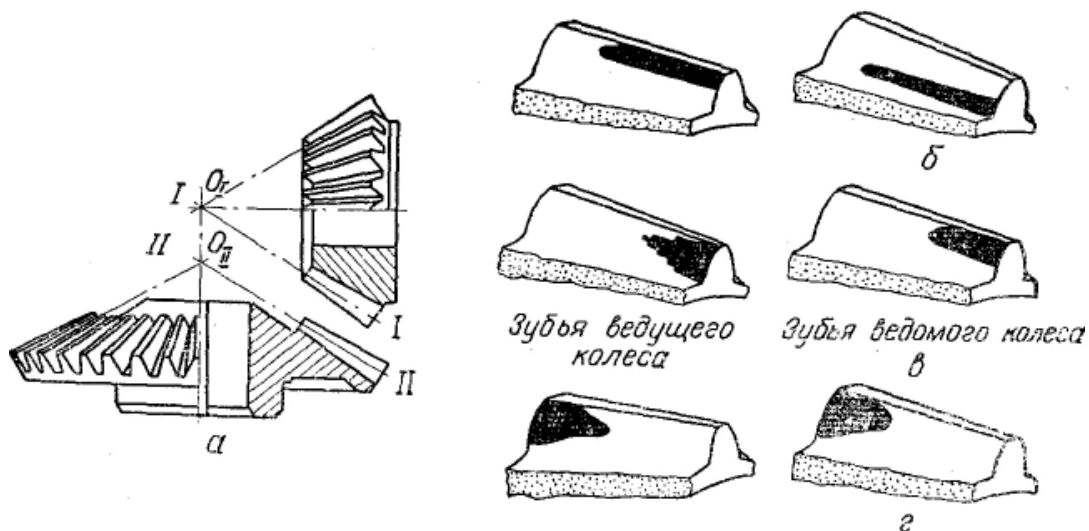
Похибка збірки конічної зубчатої передачі.
